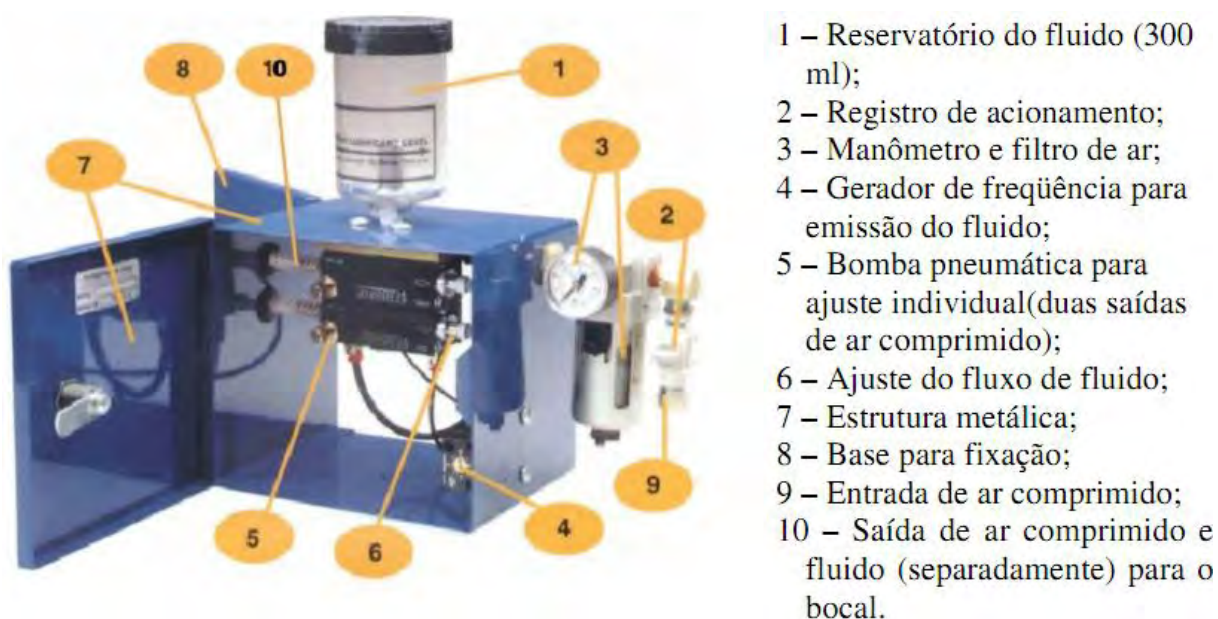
Detalhes construtivos do aplicador ITW Accu-lube 79053D.
